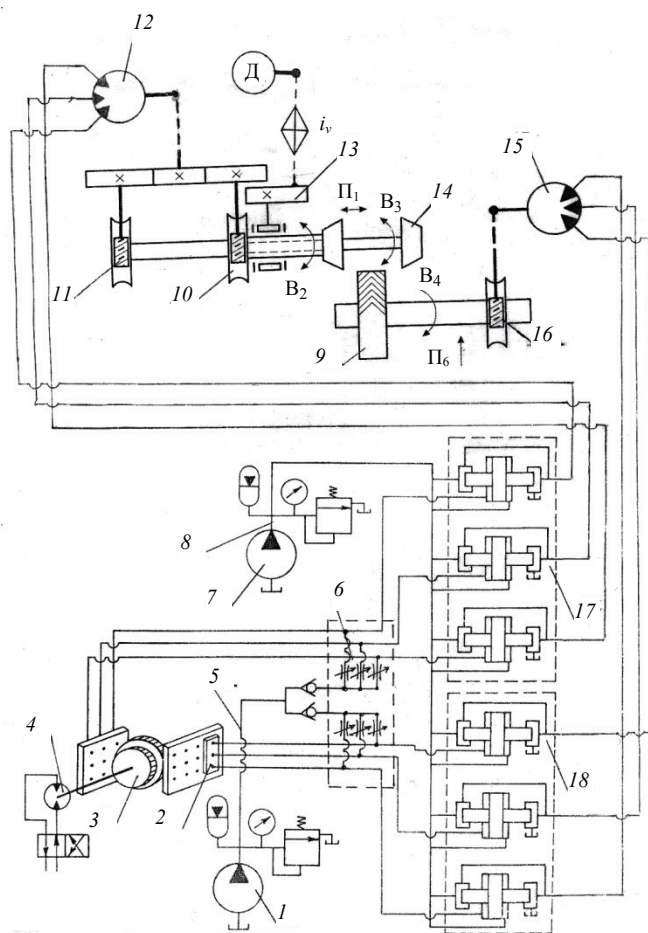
Структурная схема зубодолбежного станка с гидравлическими формообразующими связями для нарезания зубьев шевронных зубчатых колес двумя зуборезными долбьями
